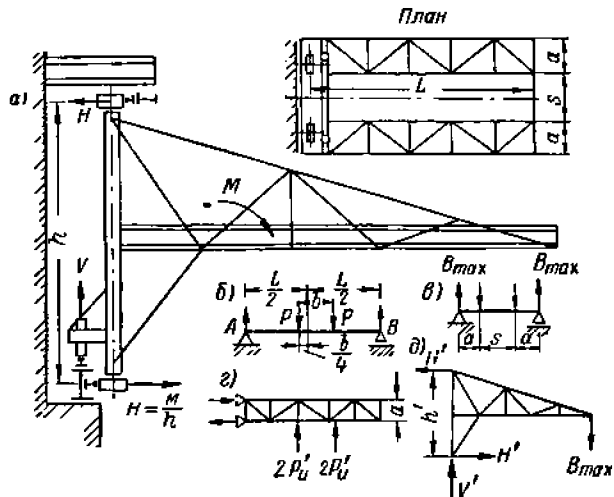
Расчетные схемы консольного крана: а — общей конструкции; б — подрельсовой двутавровой балки; в — торцевой швеллерной балки; г — горизонтальной фермы связей; д — боковой фермы
